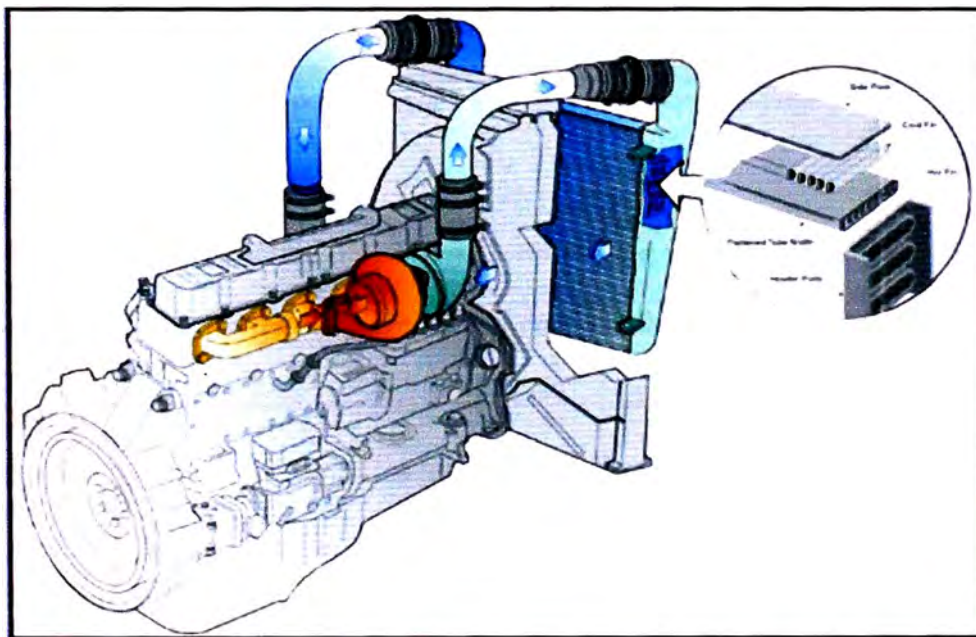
Vista de equipo posenfriador y los turbocompresores de un motor.
